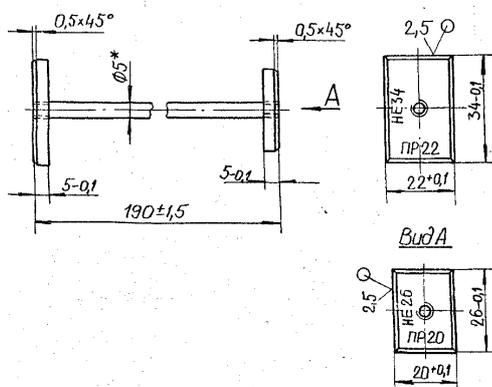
Шаблон для контроля размеров разрыва основных и дугогасительных силовых контактов.
